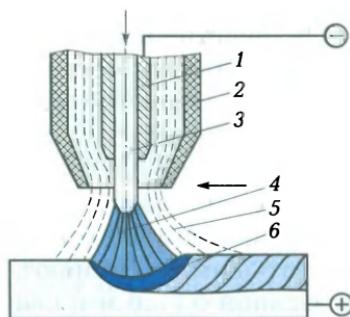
Схема сварки в атмосфере защитных газов:
